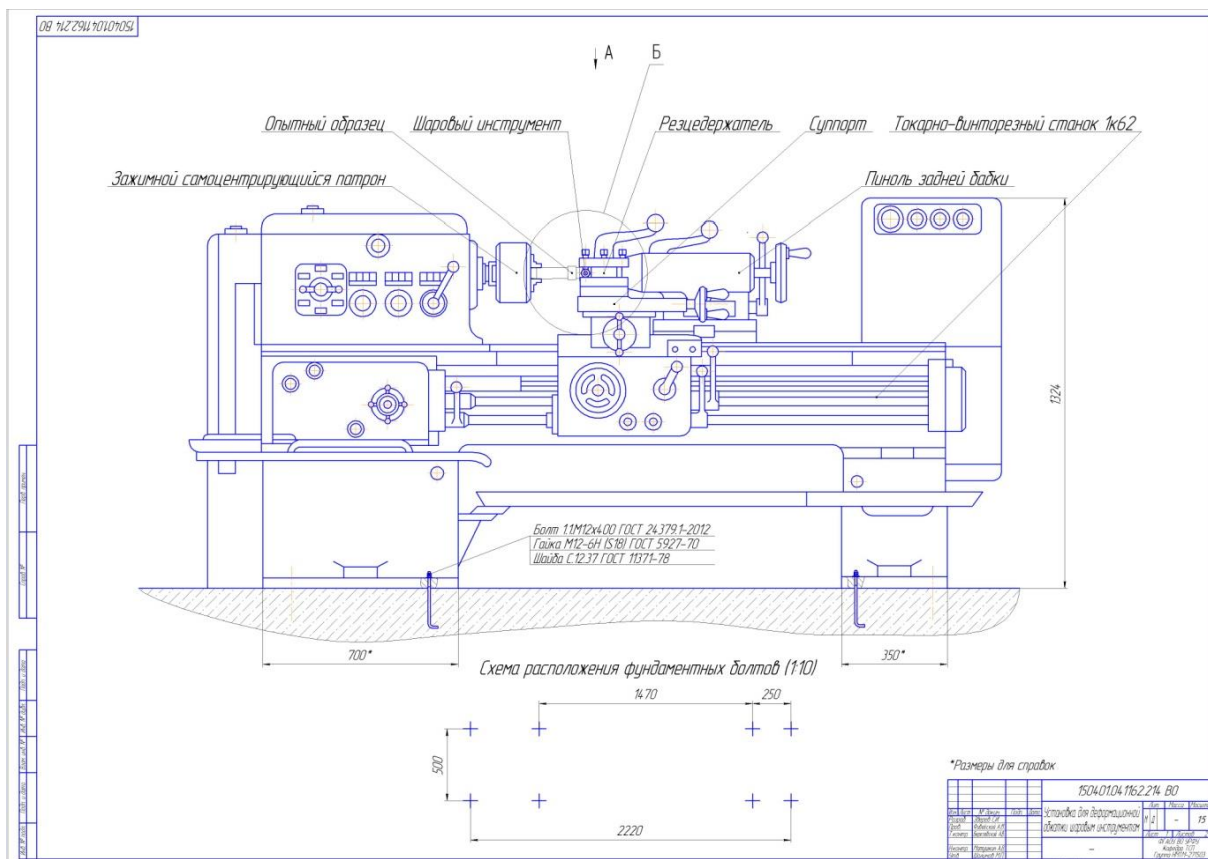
Загальний вигляд установки для деформаційної обкатки кульовим інструментом, лист 1
